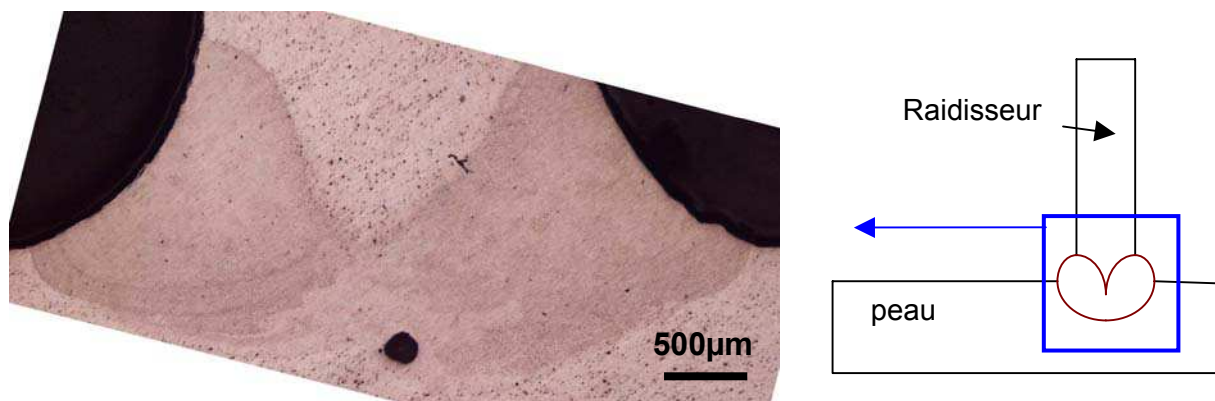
Vue générale d'une soudure en T (soudure n°1)
